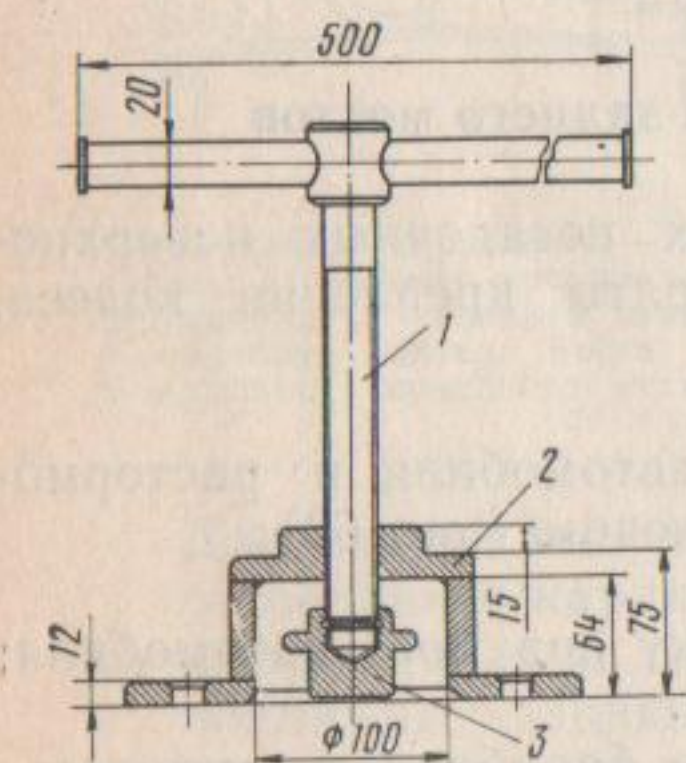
Приспособление для снятия ступицы заднего колеса:
